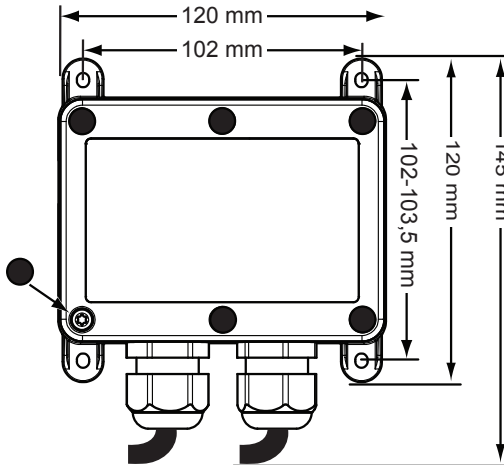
Der Empfänger ist mit 4-mm-Schrauben zu befestigen, die der Umgebung angemessen sind.
